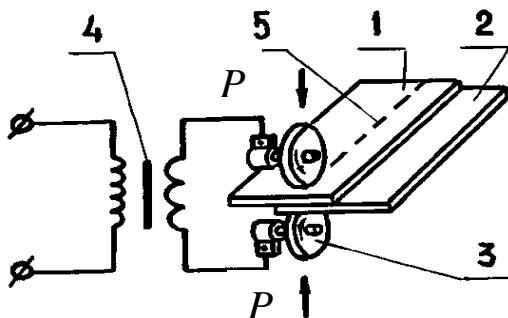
Принципиальная схема шовной сварки: 1, 2 – заготовки; 3 – электроды (ролики); 4 – трансформатор; 5 – сварочный шов
